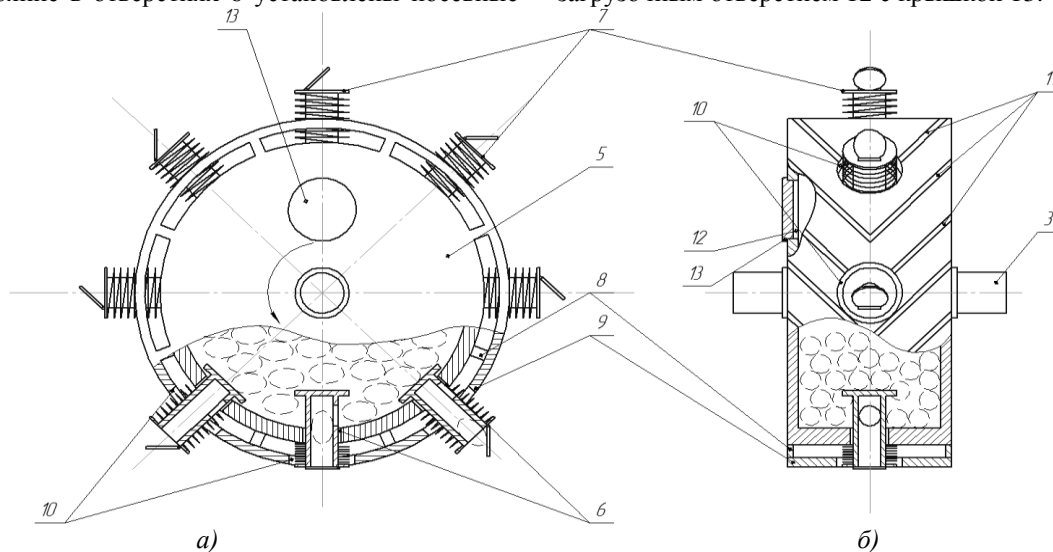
Высевающее устройство: а) главный вид, б) вид сбоку.
